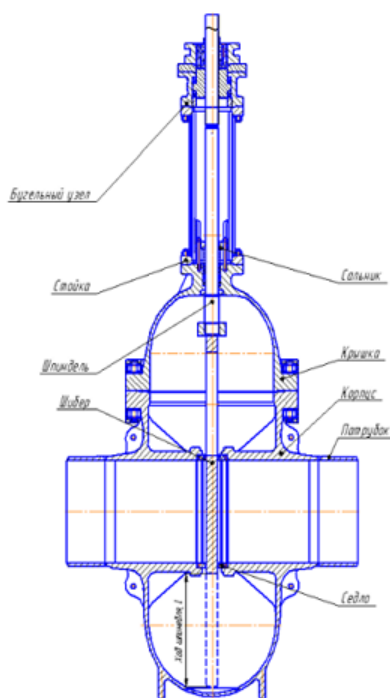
Общий вид конструкции задвижки шиберной
